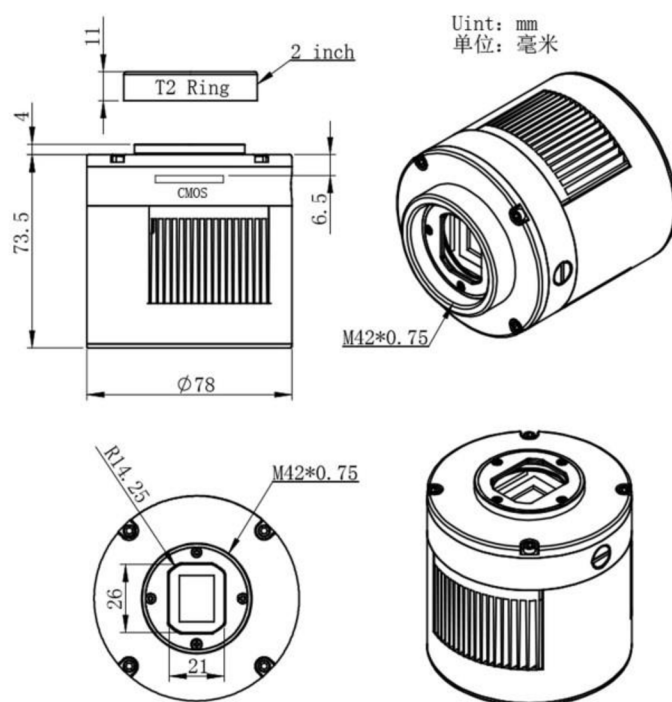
Kamera ZWO ASI 1600MM (9)
